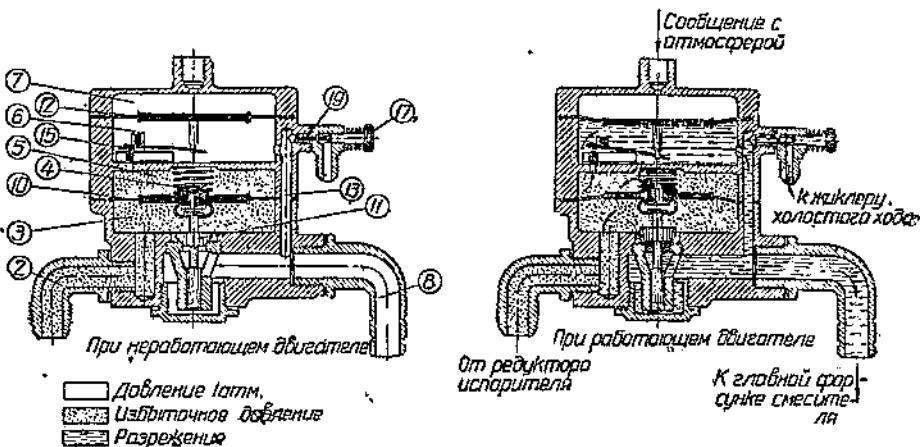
Принципиальная схема редуктора низкого давления конструкции СГ-32
